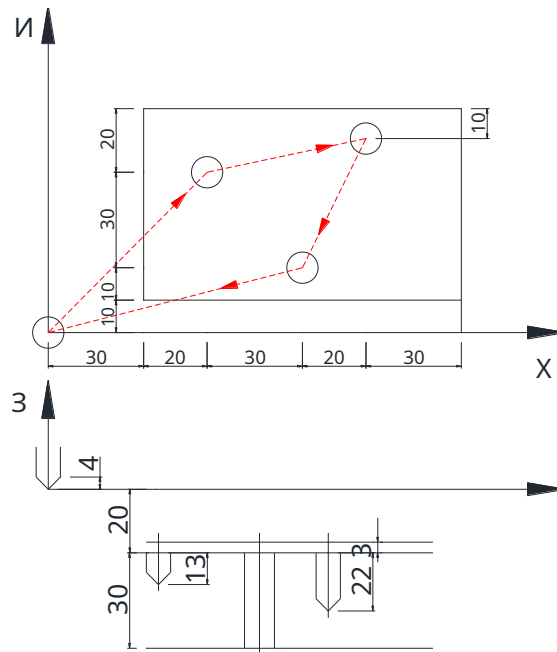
Эскиз 1 процесса обработки заготовки
